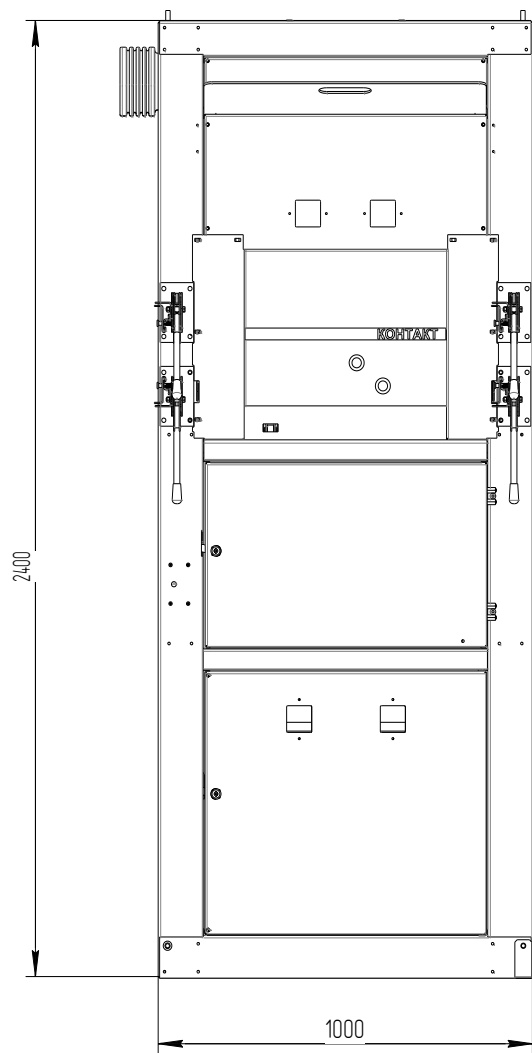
Габаритные размеры камеры КСО - 203 - 06
